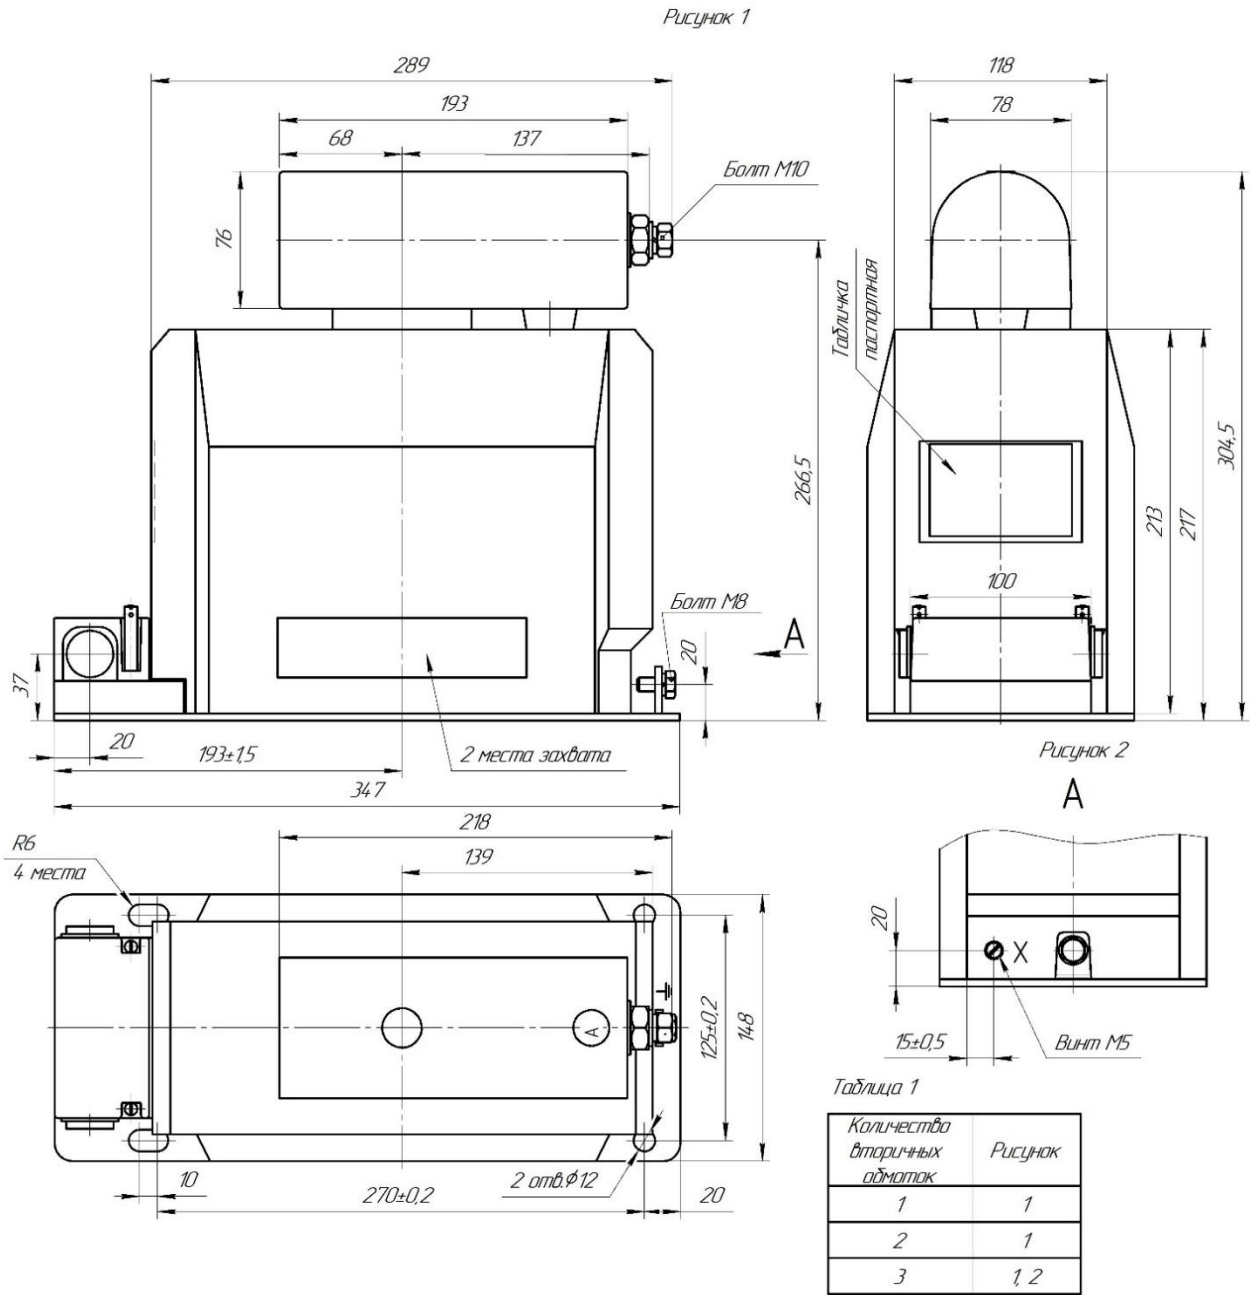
Габаритные, установочные и присоединительные размеры трансформаторов напряжения ЗНОЛ-СЭЩ-6-1 и ЗНОЛ-СЭЩ-10-1
